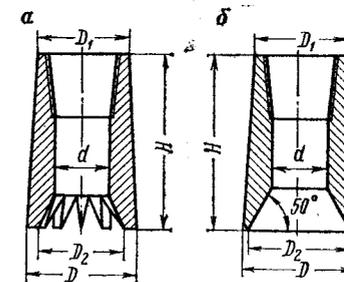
Башмаки: а — фрезерный; б — гладкий
